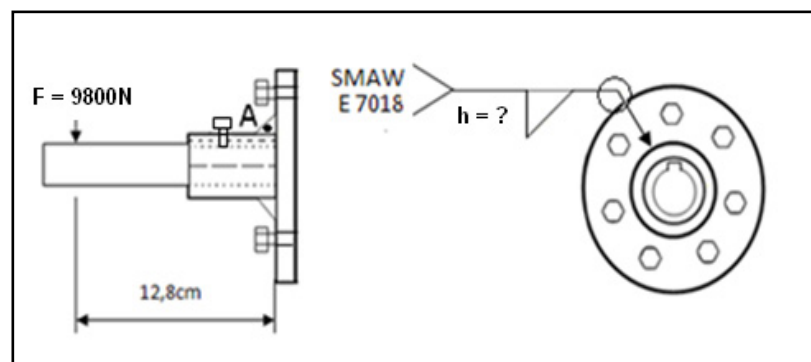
BOSQUEJO DE LOS ACOPLE QUE SERAN SOLDADOS
